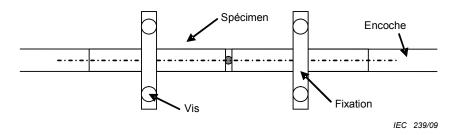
Illustration schématique du gabarit de fixation pour braser le joint de soudure seul
